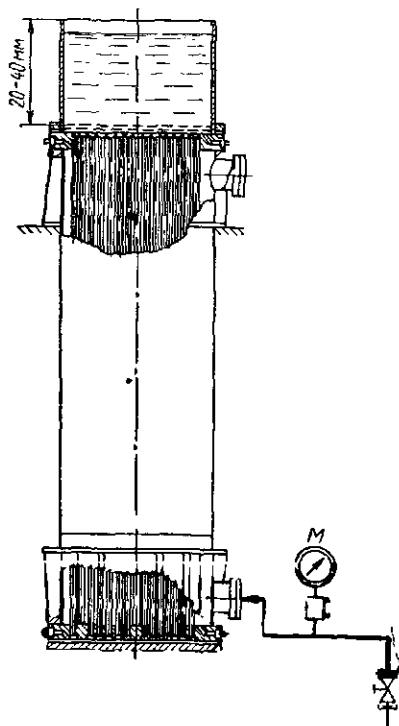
Схема установки аппарата для определения качества закрепления трубок.
